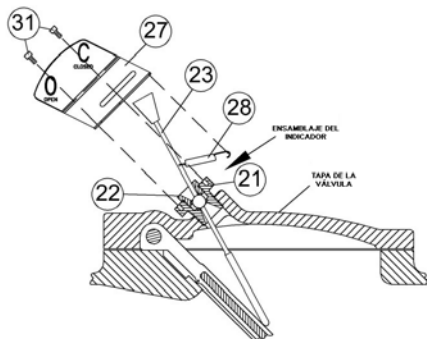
ENSAMBLADO DEL INDICADOR MECÁNICO
